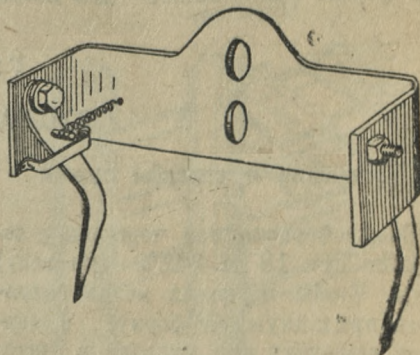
Приспособление для обрезки продольных краёв черепицы
